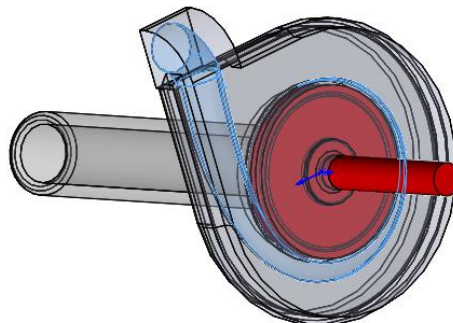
Laufrad mit Pumpenaufbau für Pretests
